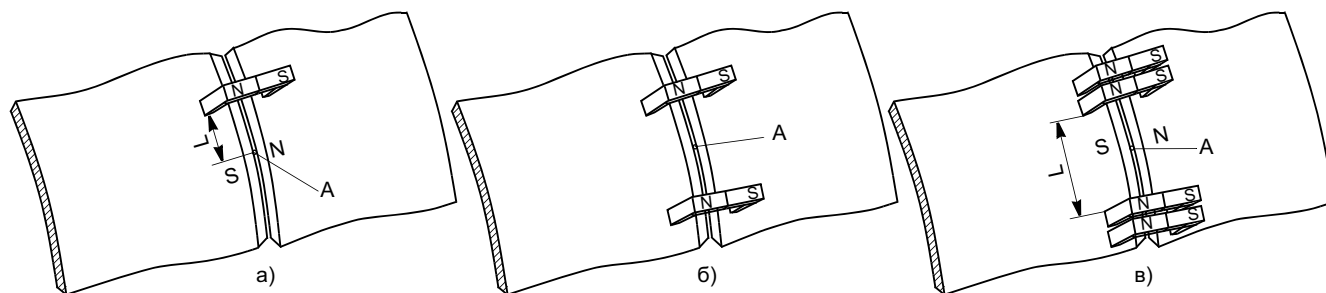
Схема установки одного (а), двух, симметрично отстоящих от зоны сварки (б) и расположенных попарно, симметрично от зоны сварки (в) постоянных компенсационных магнитов (А — зона сварки)
